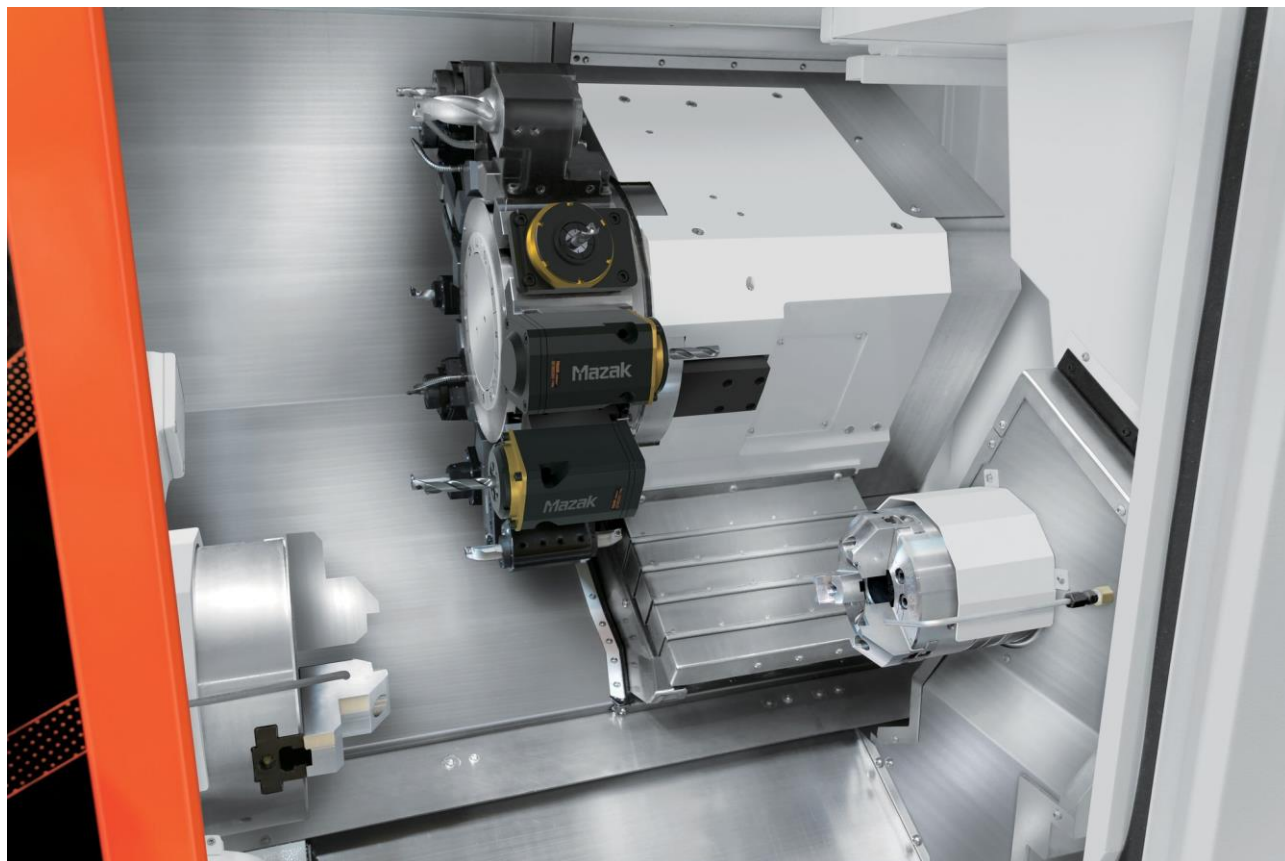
Токарний центр з ЧПУ Mazak QUICK TURN 250MSY
